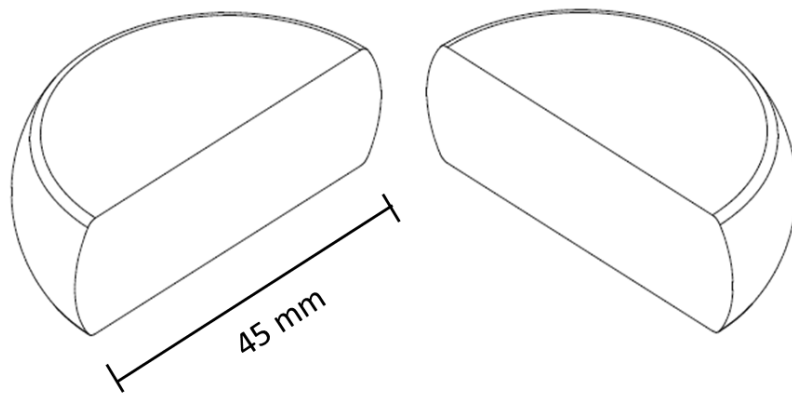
Corte transversal de probetas deformadas para su análisis.
